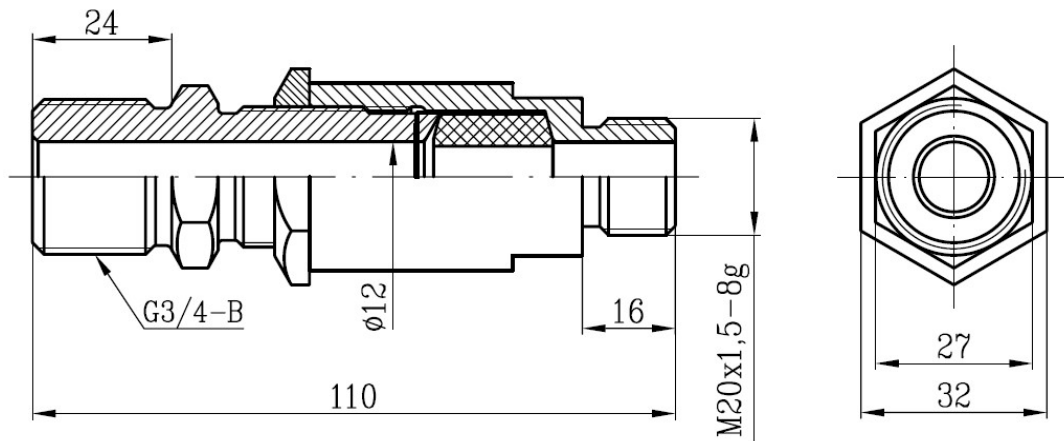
Ввод кабельный для трубного монтажа (ТБ 3/4")
